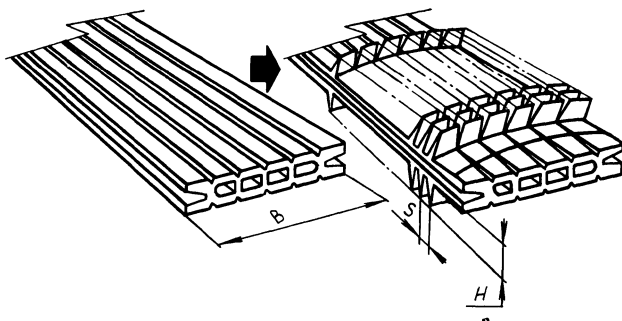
Вид заготовки и оребренного плоского элемента с криволинейными рядами ребер
